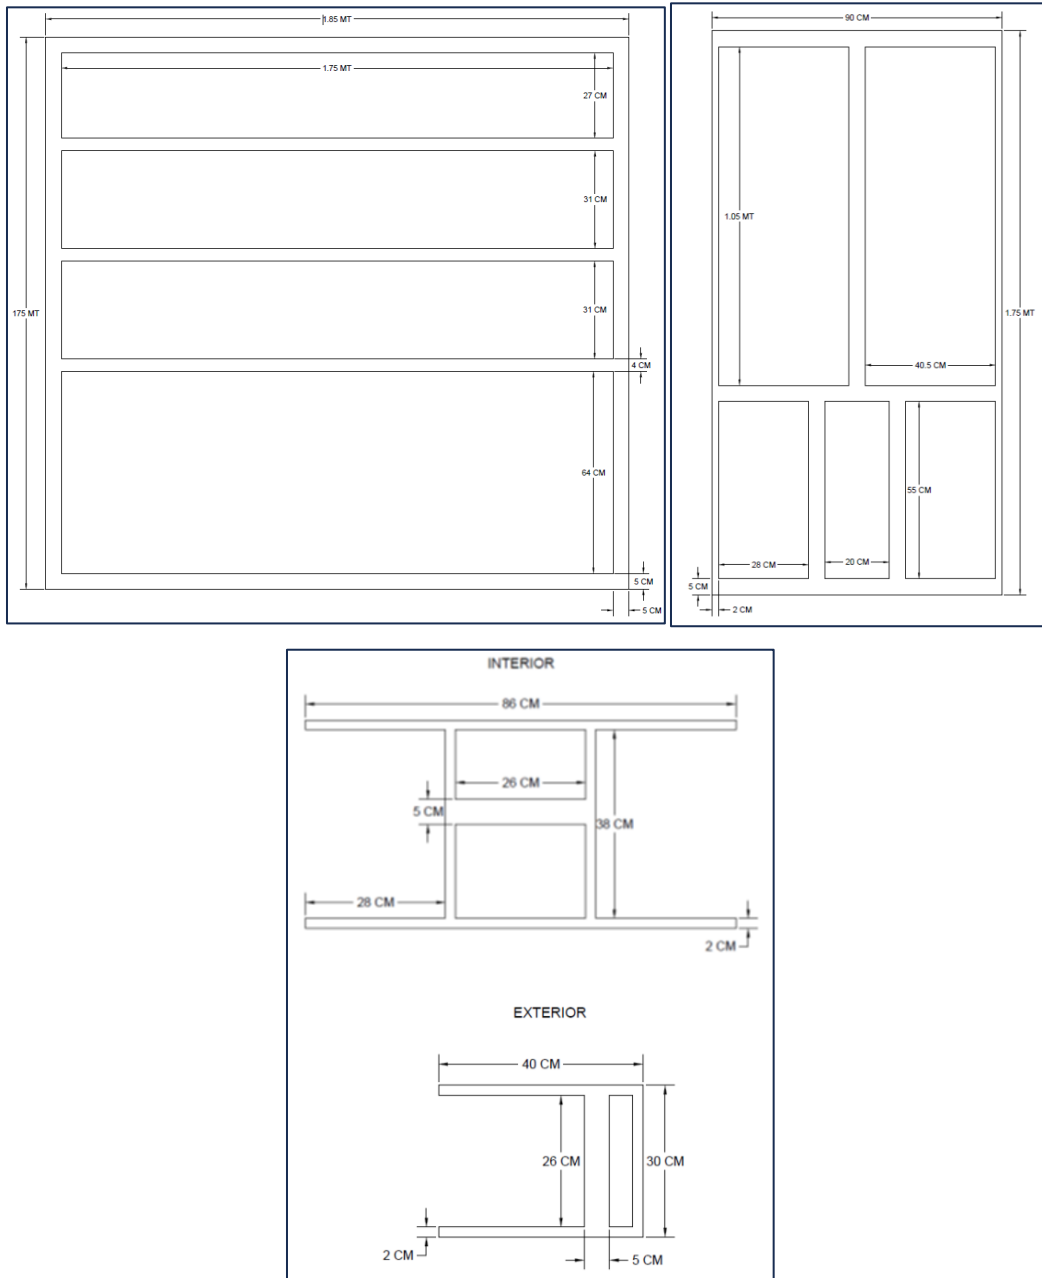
Dimensiones de la vista de frente y de lado de la estructura, detalle interior y exterior.
